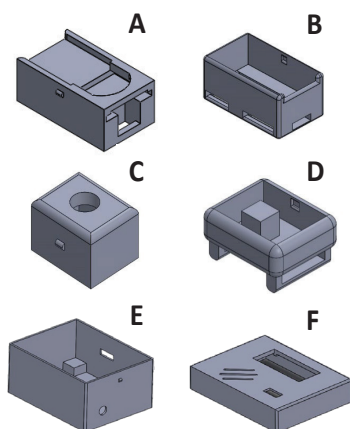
Vistas isométricas de las piezas de soporte. (A) Vista isométrica de la pieza superior de soporte del Sensor MAX30102, (B) pieza inferior de soporte del Sensor MAX30102, (C) pieza superior de soporte del sensor MLX90614, (D) pieza inferior de soporte del sensor MLX90614, (E) pieza inferior del contenedor del sistema y (F) pieza superior del contenedor del sistema
